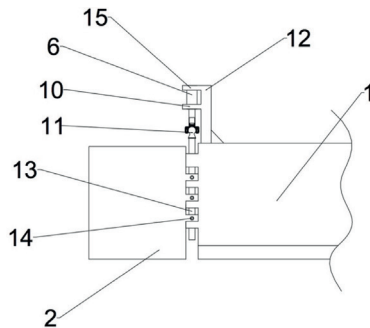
Приближенный вид механизма подъема открывков (опущенные открывки)
